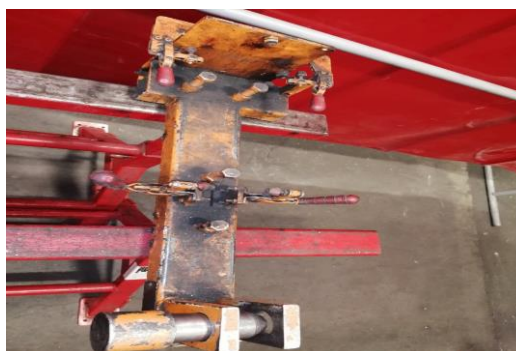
Приспособления для сборки и сварки удлинителя
